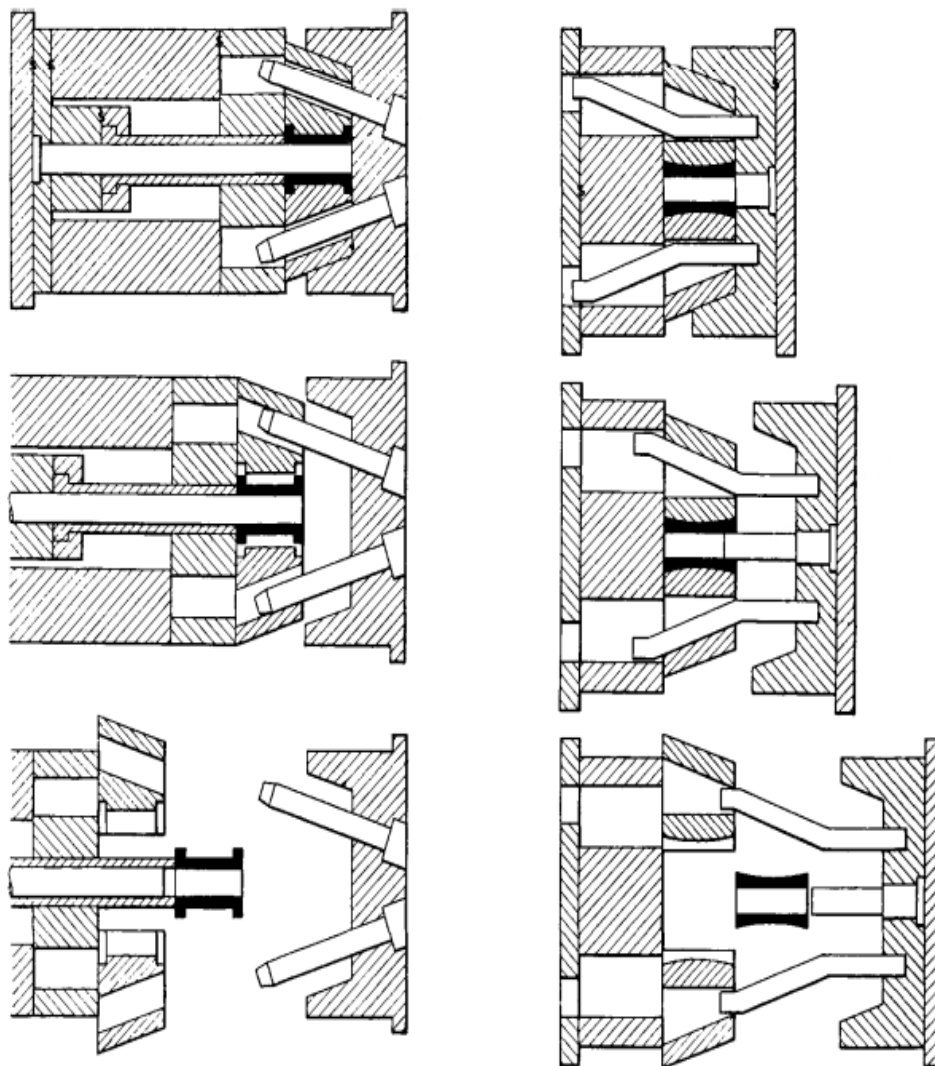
Izquierda: pernos inclinados. Derecha: correderas acodadas. Fuente: How to make injection molds [7].
